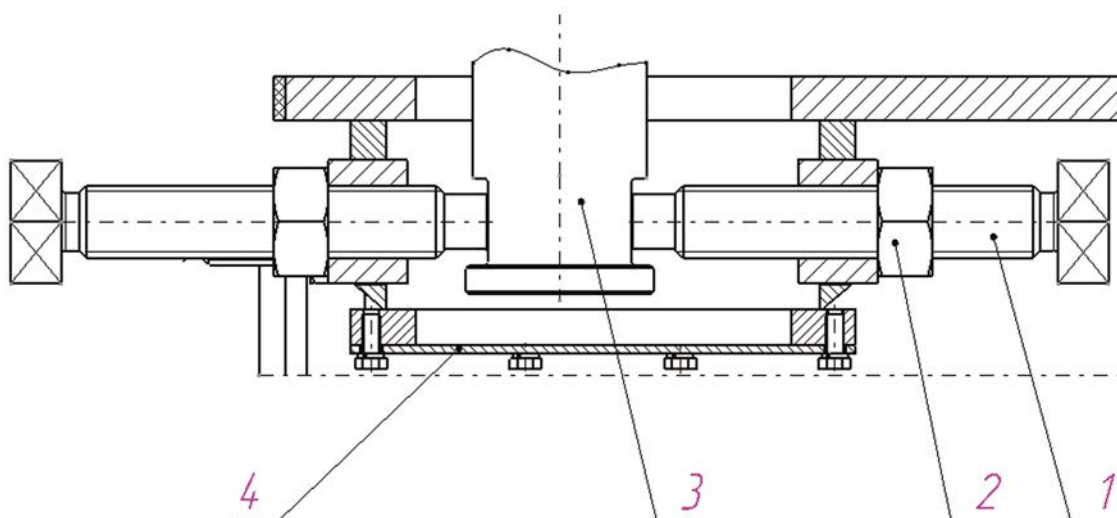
Механизм регулировки положения отбойной плиты и решетки колосниковой относительно ротора
